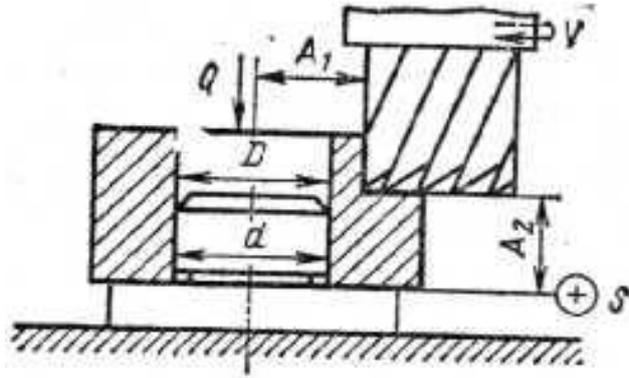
Схема фрезерования втулки (к задаче 3.1)
